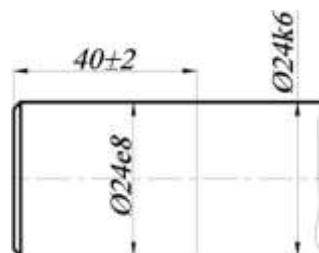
Пример нанесения номинальных размеров и полей допусков вала
